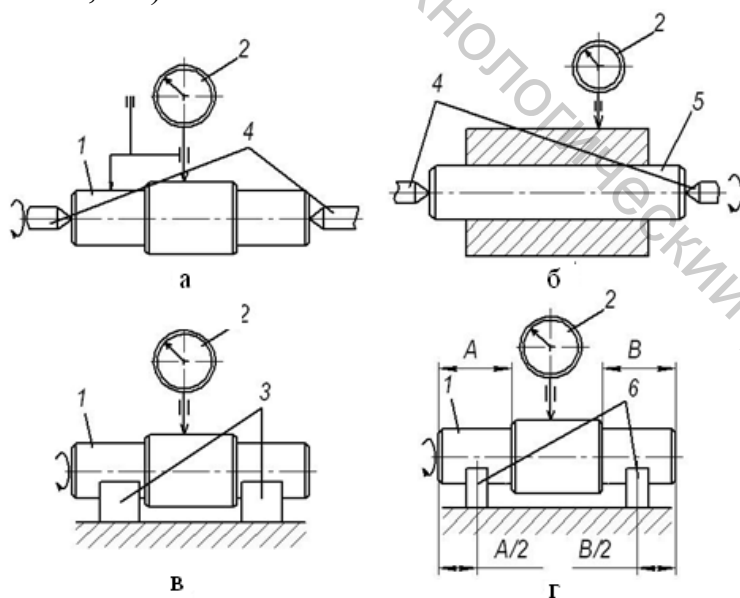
Схемы измерения радиального измерения при базировании: а – в центрах, б – на оправке, в – на призмах; г – на ножевых призмах; 1 – контролируемая деталь; 2 – индикаторная головка; 3 – призмы; 4 – центры; 5 – оправка; 6 – ножевые призмы
